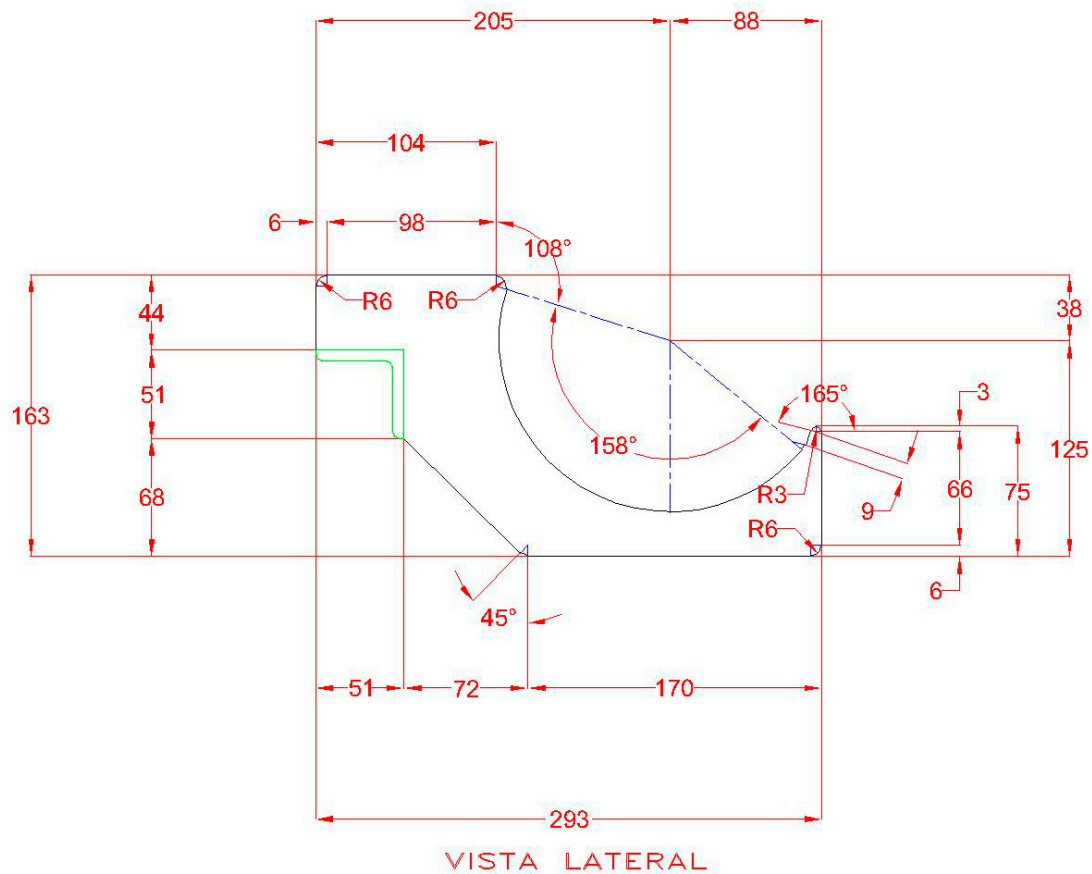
Propuesta #2 de gancho de sujeción. (Cotas en mm)
